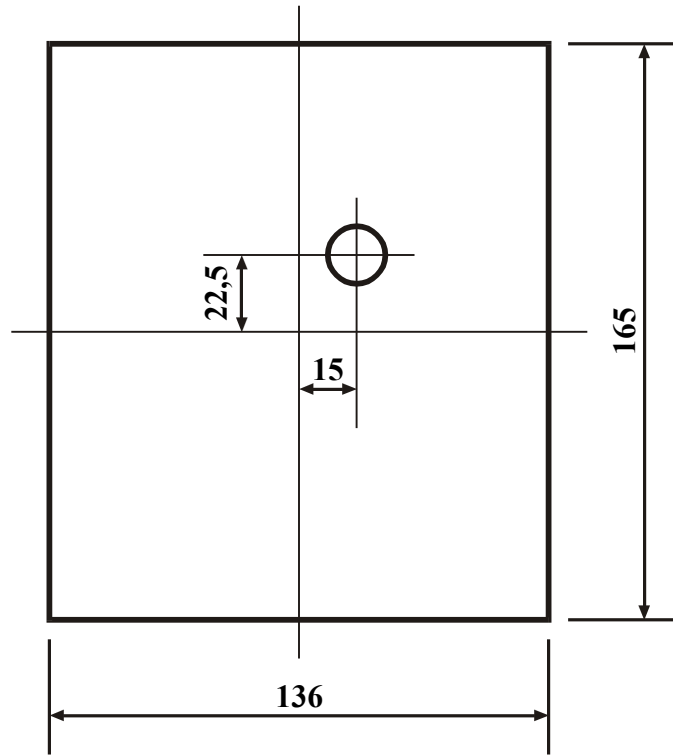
Baffle padrão, dimensões (Seção 11)
